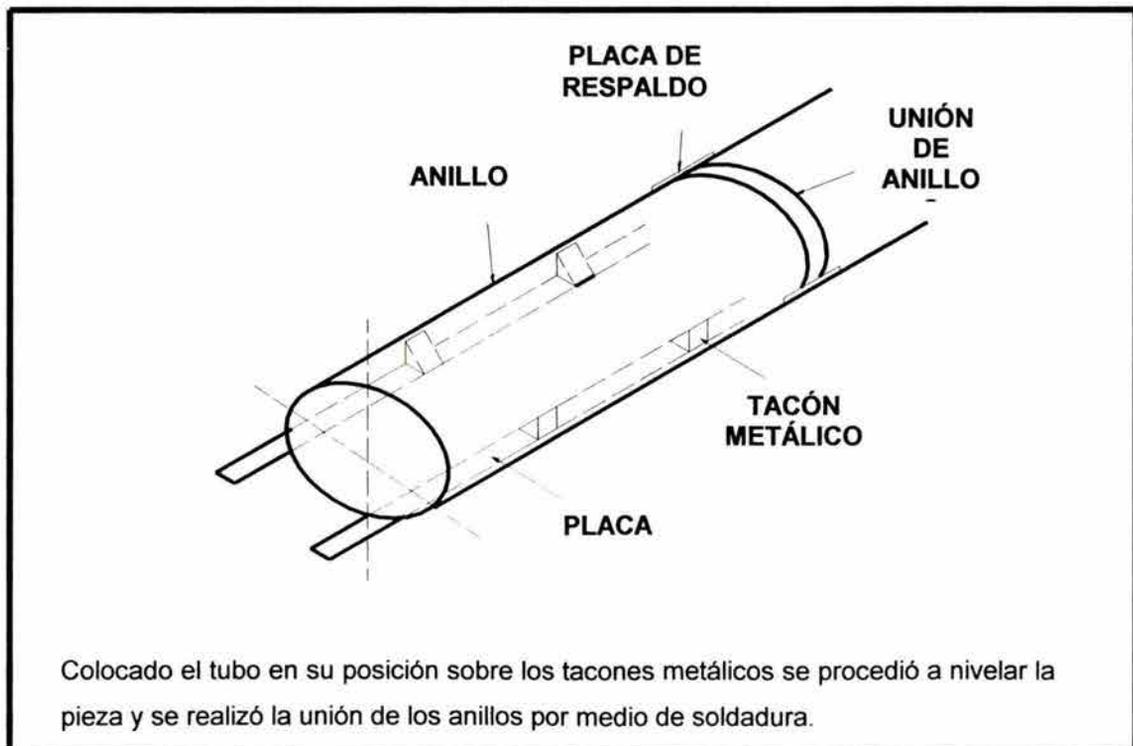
COLOCACIÓN DE GUÍAS INTERIORES
